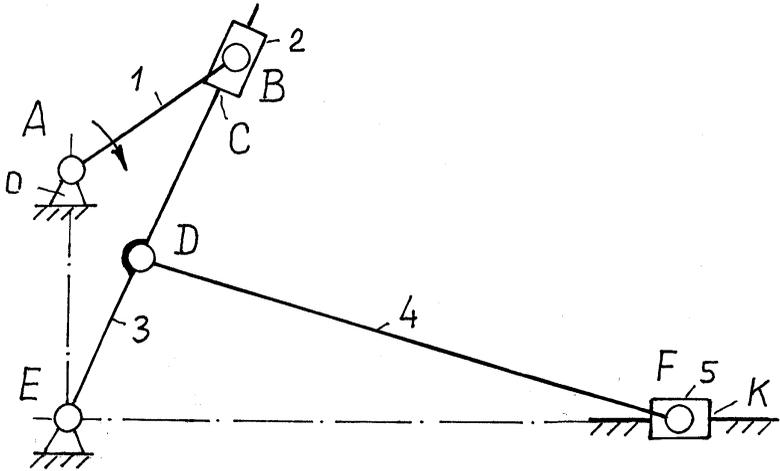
Кинематическая схема шестизвенного плоского кулисный механизма
